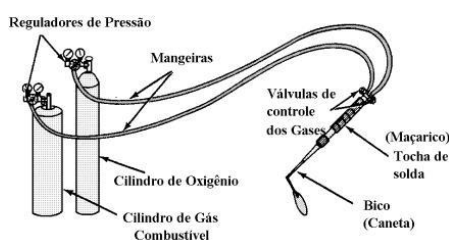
Esquema de soldadura por oxi-gás.
